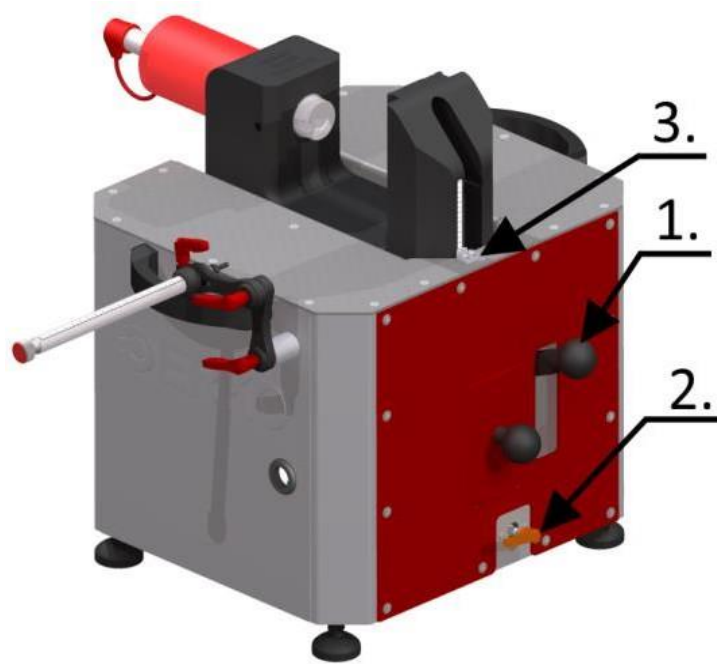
Компоненти пристрою: 1 — важіль підйому корпусу, 2 — важіль опускання корпусу, 3 — індикатор положення корпусу.
